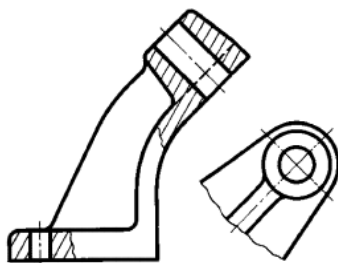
Дополнительный вид, необозначенный на чертеже
